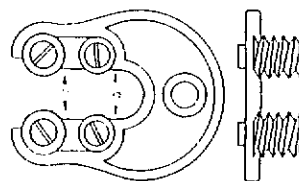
Calibre de herradura para rocas con rodillos de medición. a) Lado bueno; b) lado malo.
